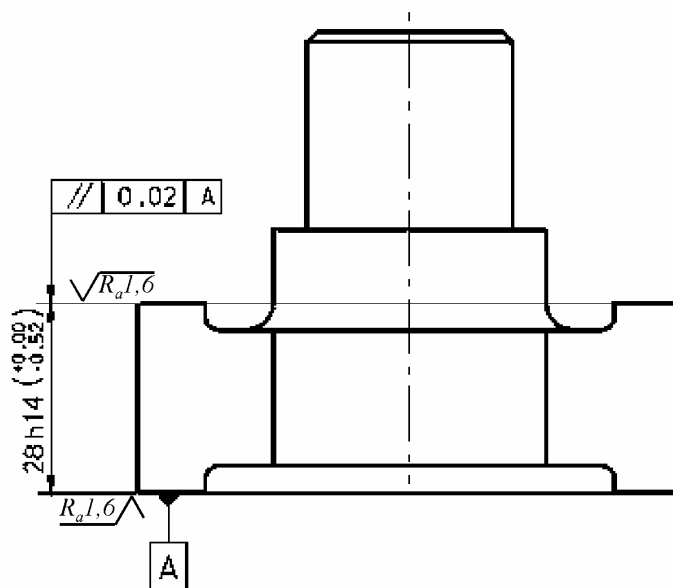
Несоответствие допуска размера допуску отклонения расположения и шероховатости поверхностей
